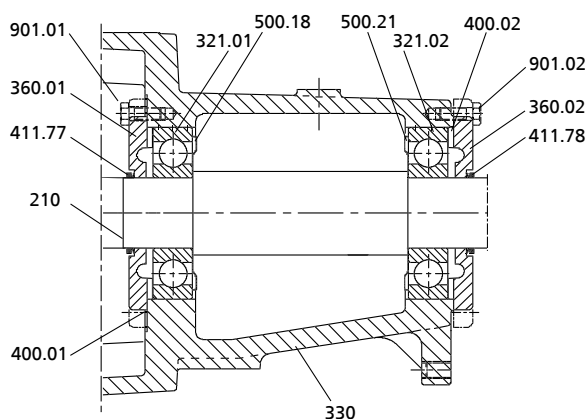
Монтаж радиальных шарикоподшипников с консистентной смазкой
